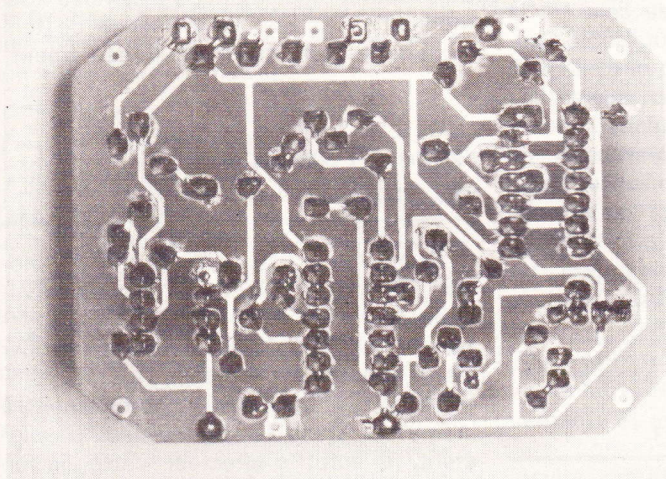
Le module, vu côté cuivre, après soudures.
